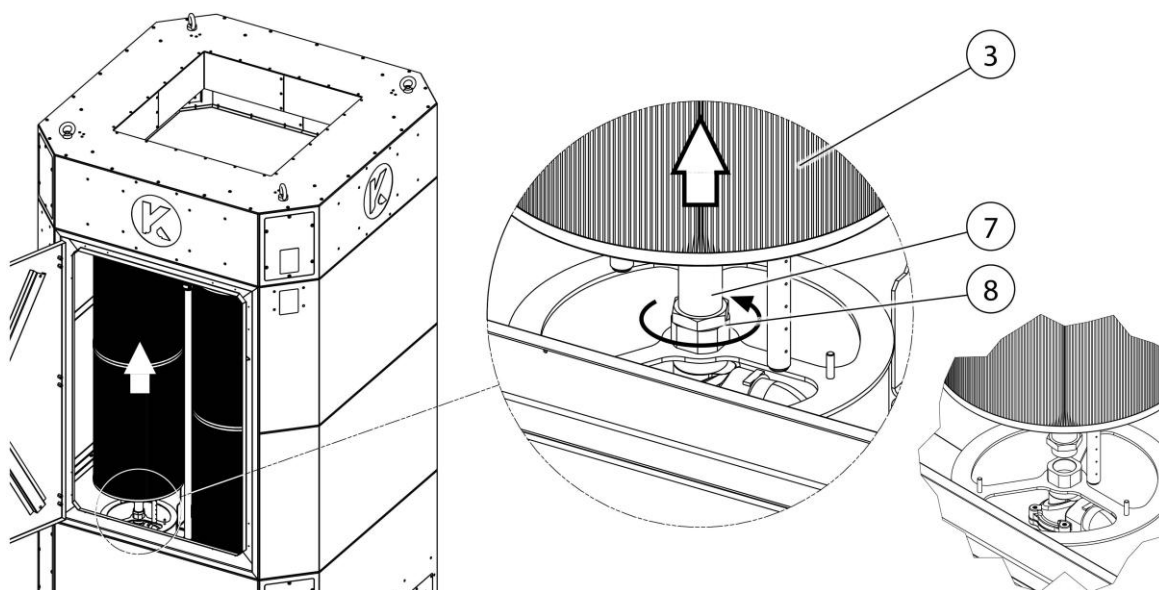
Cambio filtro - smontaggio dell'ugello rotante
